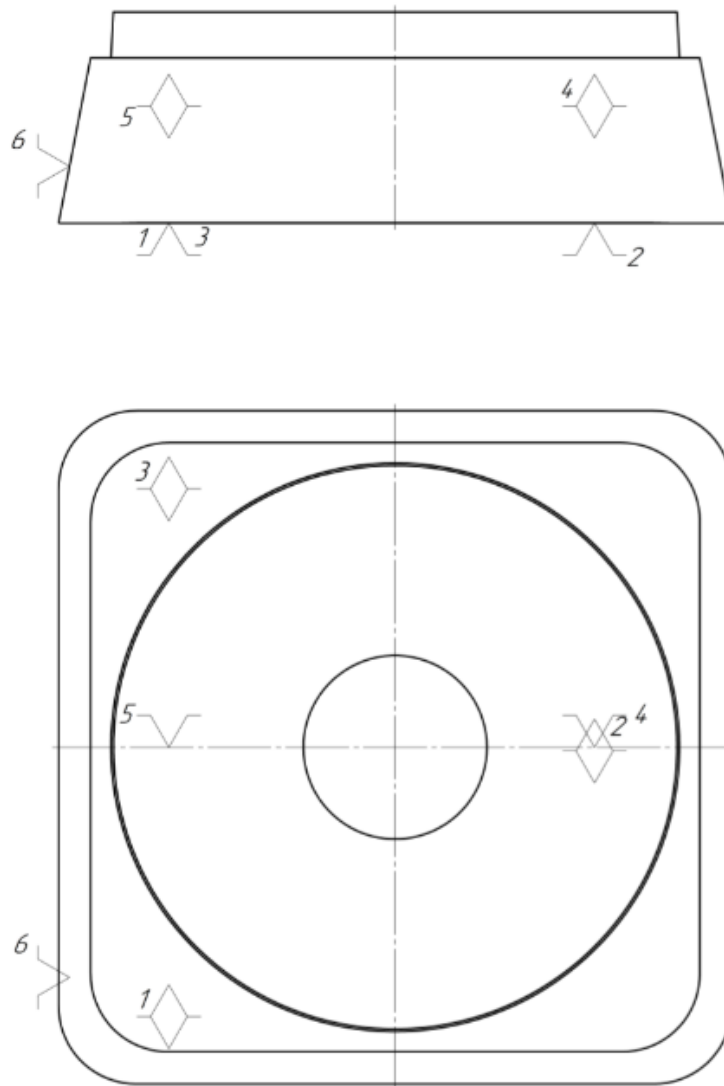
Схема базування деталі «Корпус» по ТБ 2.
